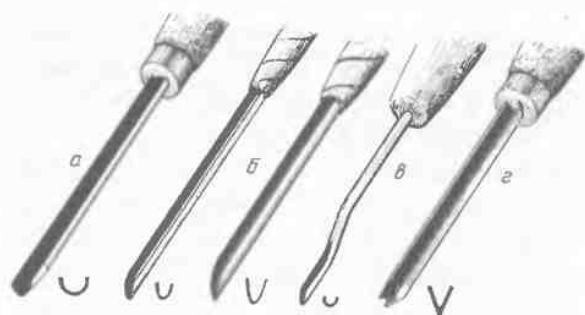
Царазики и уголок: а — стандартный; б — из растяжек зонтиков; в — выполненный сверлением отверстия в стержне; г — стандартный уголок
